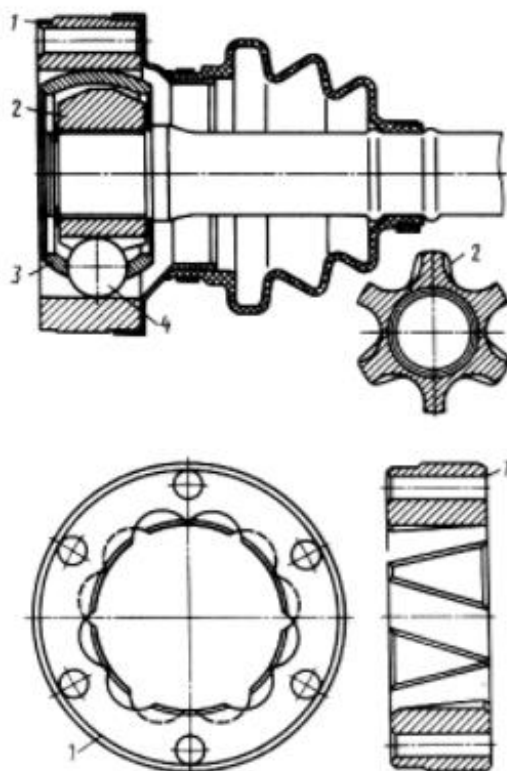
Шариковый универсальный карданный шарнир типа “Лебрю”: 1 – корпус; 2 – сферический кулак; 3 – сепаратор; 4 – шарики
